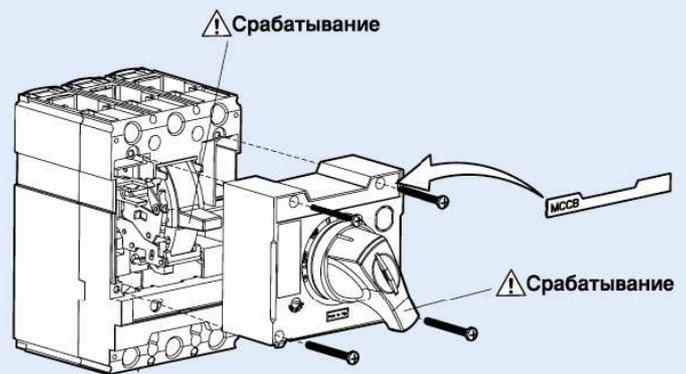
Габаритные и установочные размеры, способ установки стандартных поворотных рукояток TS100, TS160 и TS250
